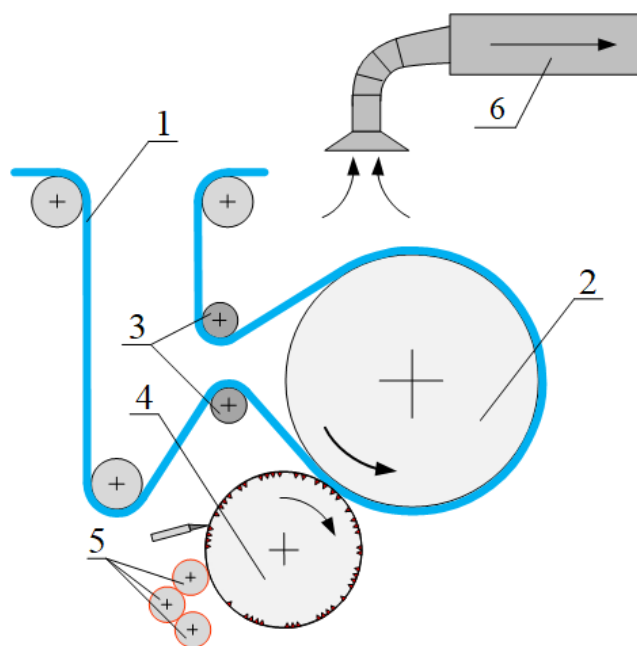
Схема узла машины для глубокой печати с валами,
